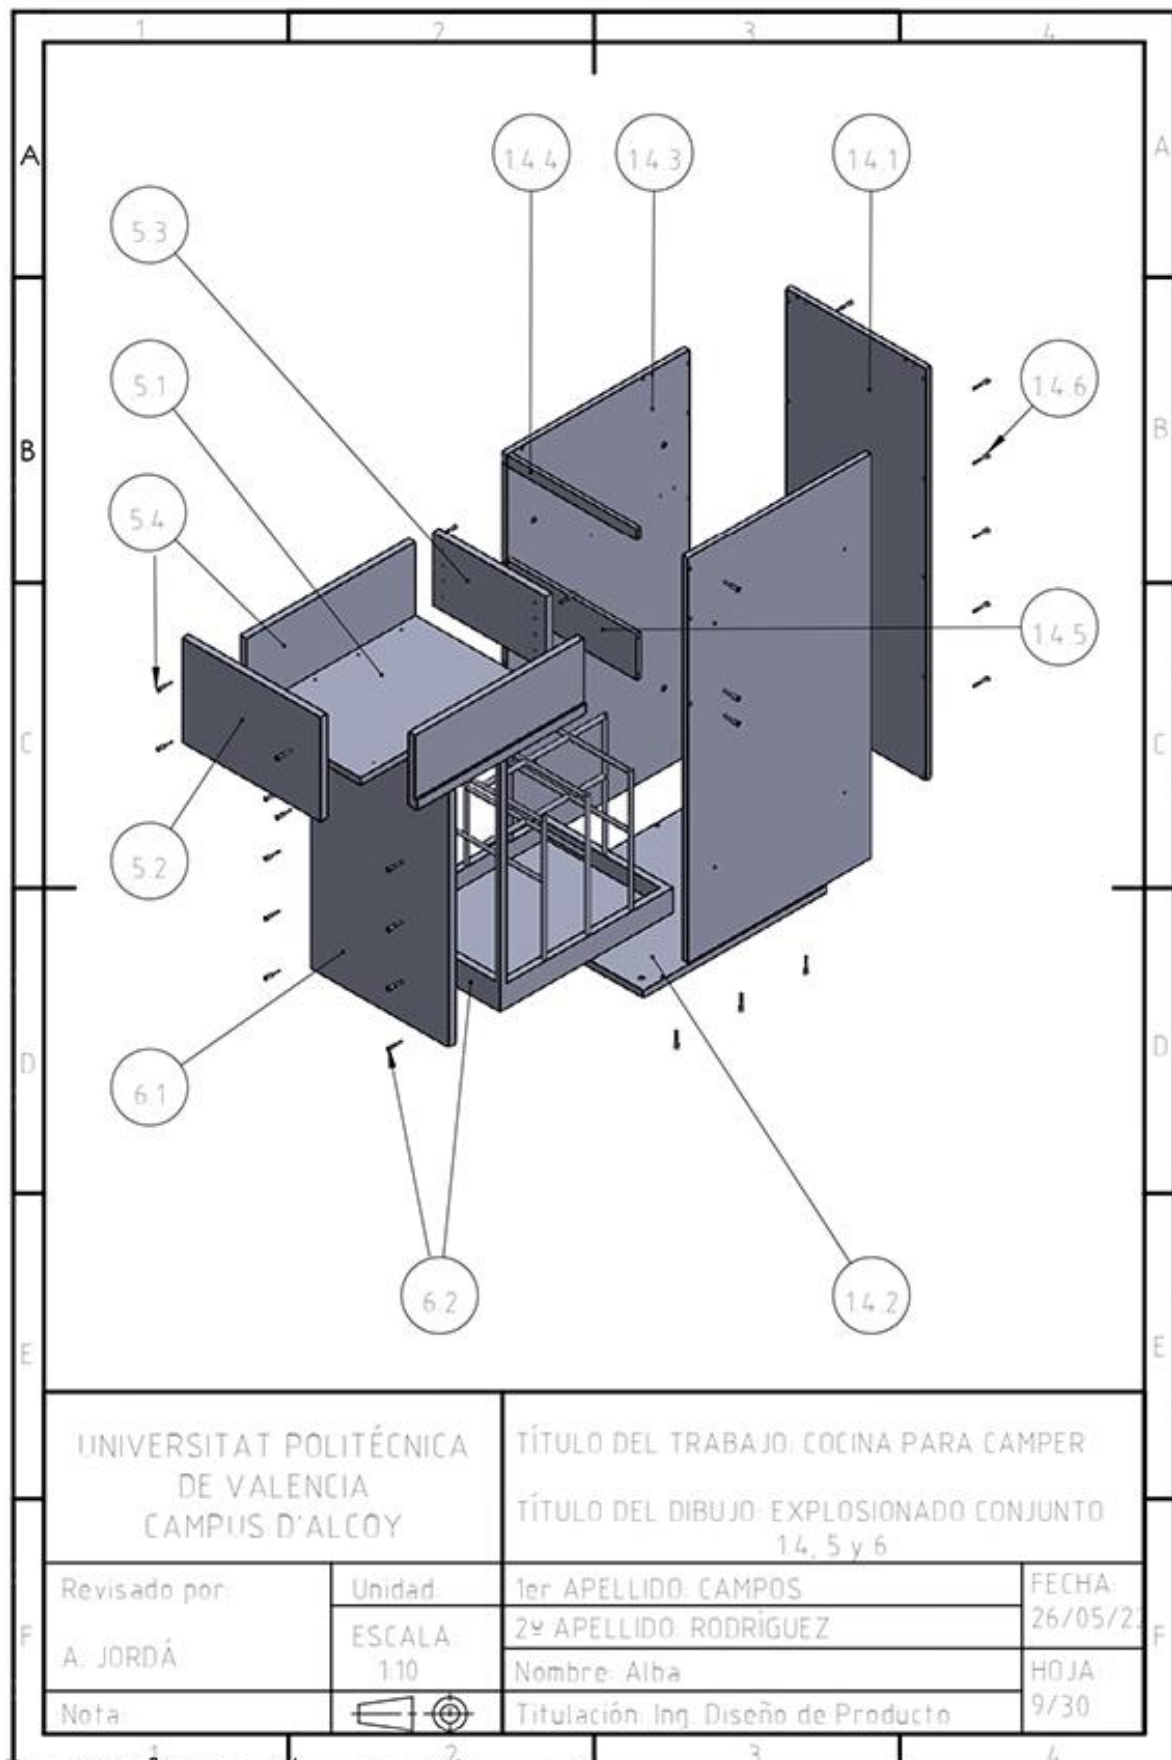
Explosionado conjunto 1.4, 5 y 6
